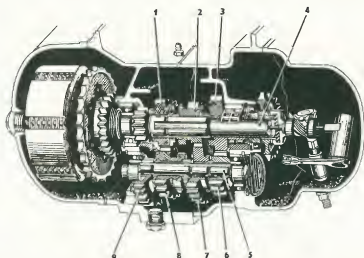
Коробка передач: 1 — неподвижная шестерня третьей передачи; 2 — подвижная шестерня второй передачи; 3 — вторичный вал; 4 — первичный вал; 5 — промежуточный вал; 6 — шестерня промежуточного вала; 7 — неподвижная шестерня второй передачи; 8 — неподвижная шестерня третьей передачи; 9 — шестерня первой передачи.
